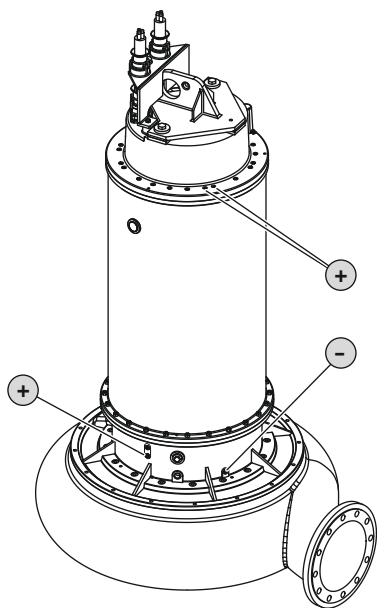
Дополнительная смазка шарикоподшипника: Т 72
